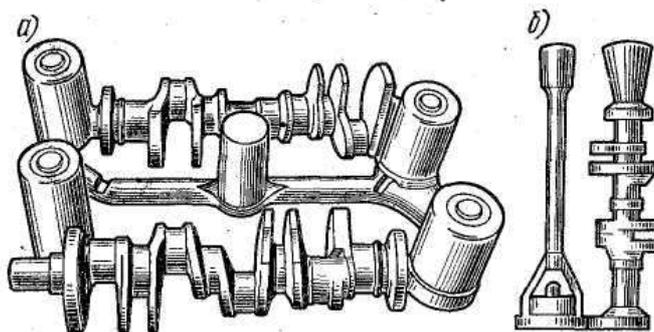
Отливка коленчатого вала в песчано-глинистую форму
